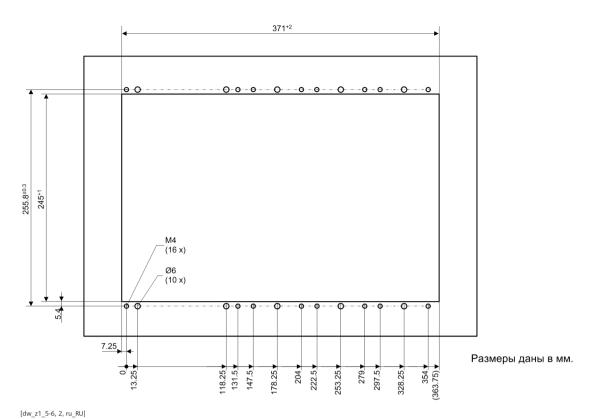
Ширина вырезов и схема сверления отверстий – устройство 5/6, первый ряд устройств
